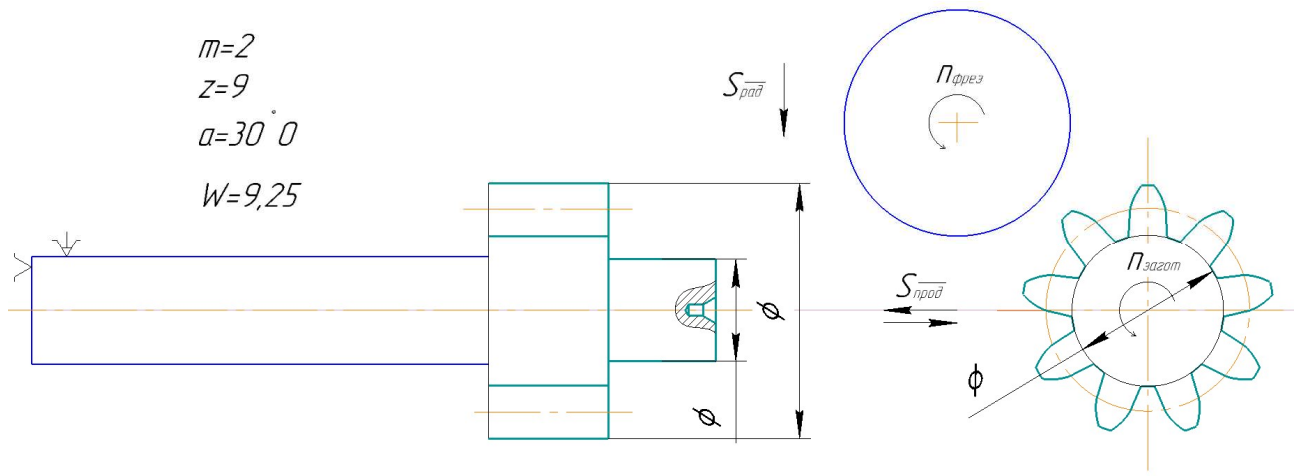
Схема обробки при зубофрезеруванні
